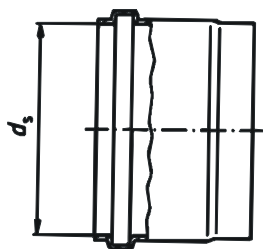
Embocadura para soldadura topo-a-topo em extremidades de tubo
